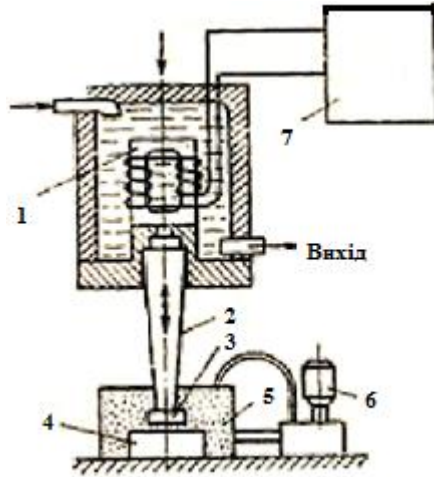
Принципова схема установки для обробки ультразвуковими коливаннями абразивних зерен
